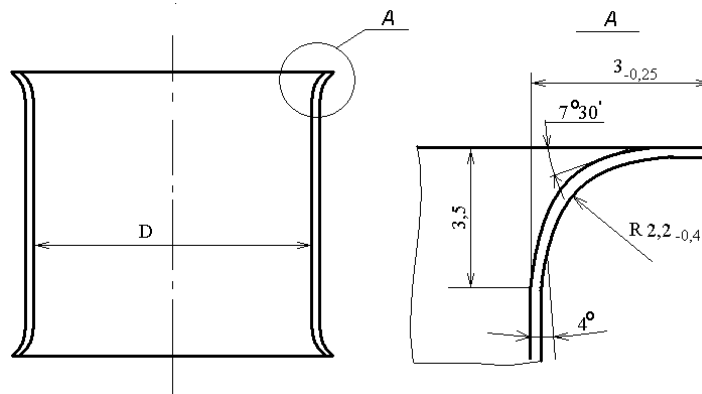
Размеры отбортовки корпуса диаметром 99 мм
